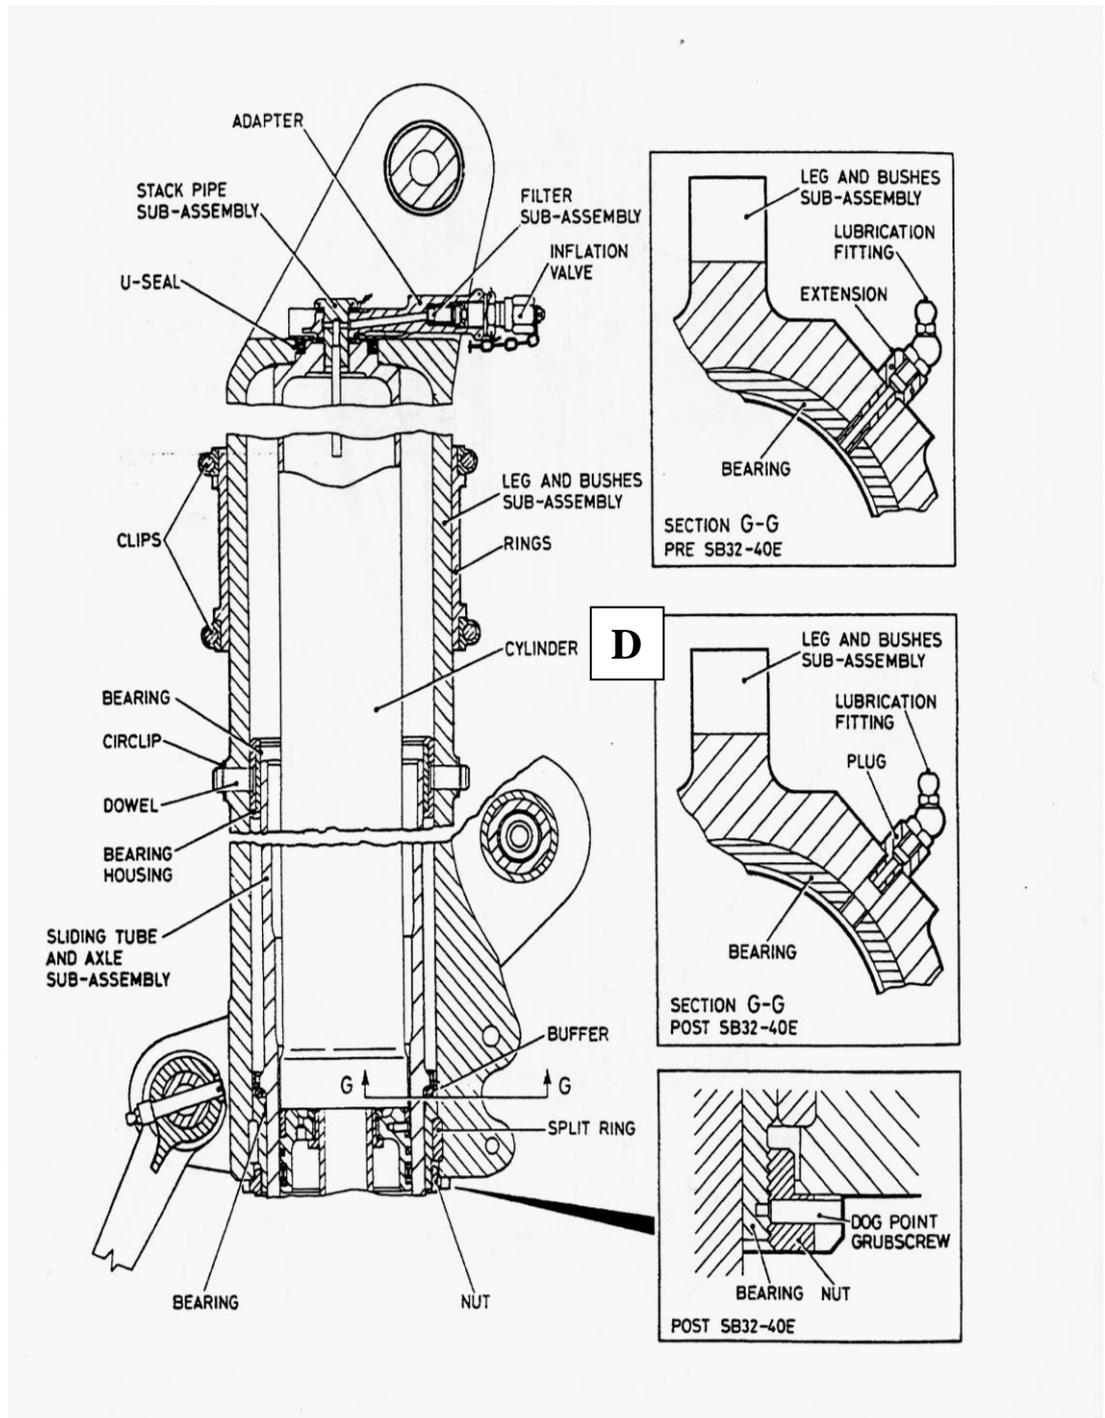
Conjunto de la pierna del tren principal de aterrizaje
